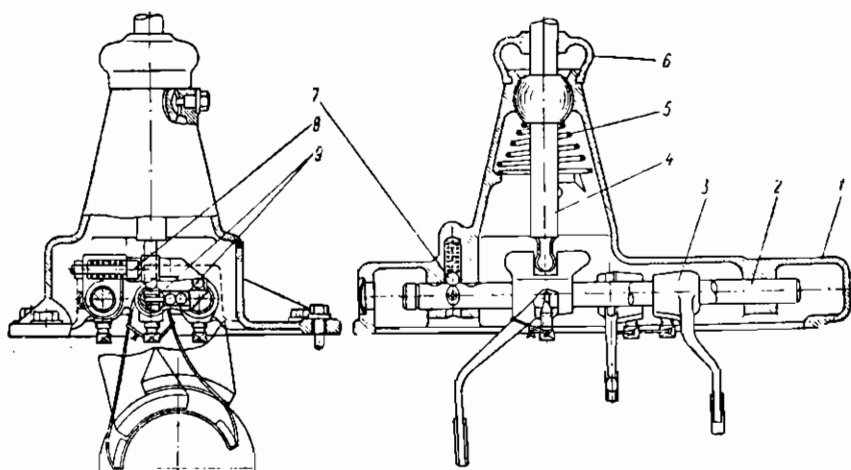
Механизм переключения шестерен коробки перемены передач: 1 — крышка коробки передач; 2 — валик; 3 — вилка; 4 — рычаг переключения; 5 — пружина; 6 — чехол; 7 — шарик фиксатора; 8 — пружинный упор; 9 — замочное устройство
